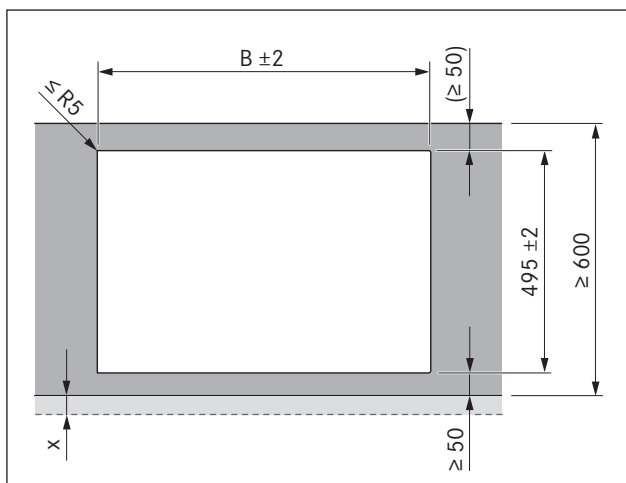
Medidas de recorte para montagem por sobreposição
